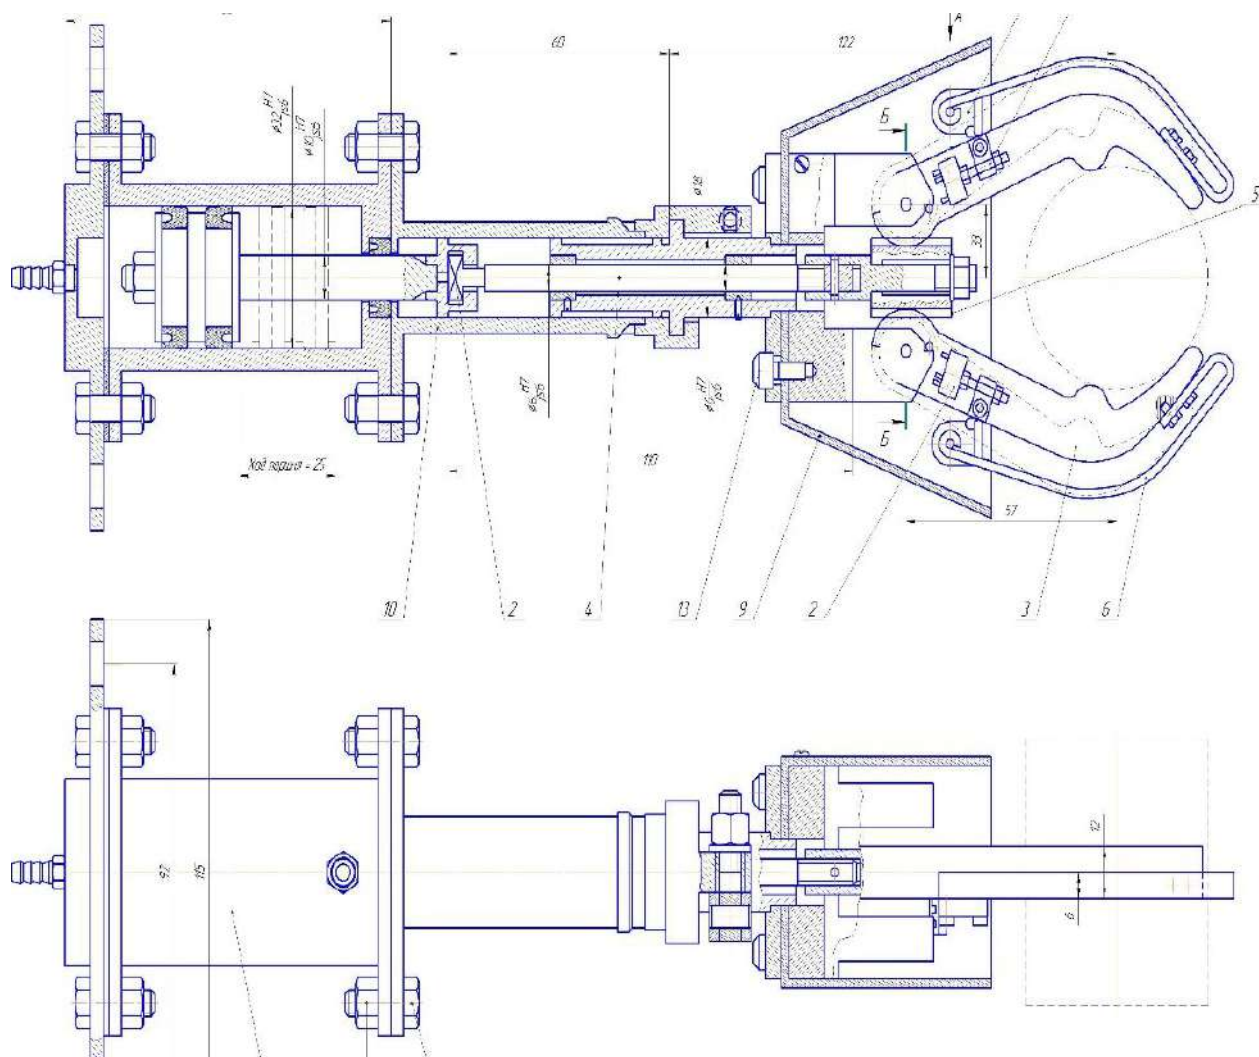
Схват для загрузки заготовки в рабочую зону станка
